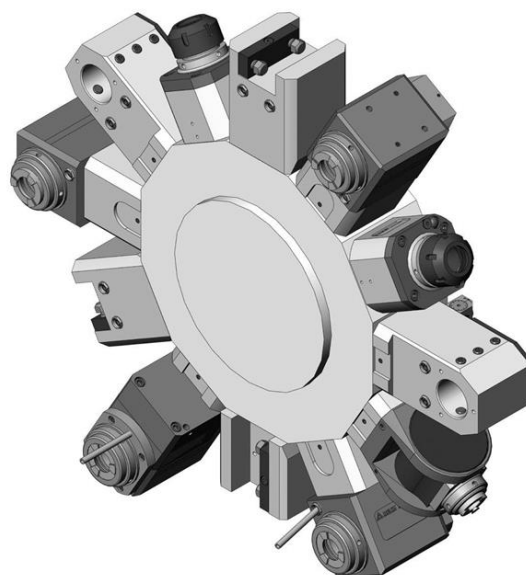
Револьверная головка VDI 12 SAUTER
